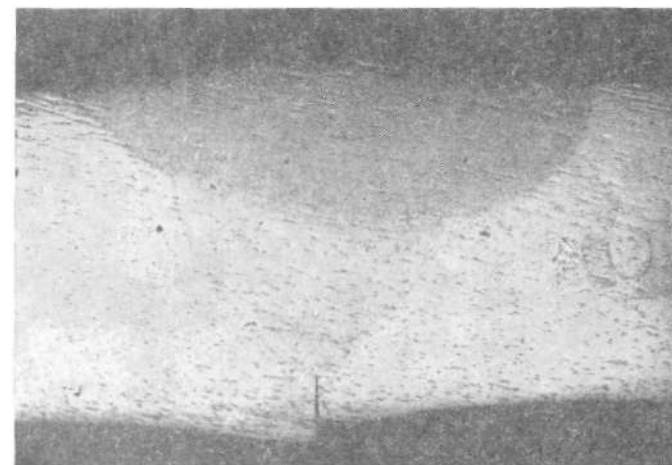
Непровар при сварке стыкового соединения.
